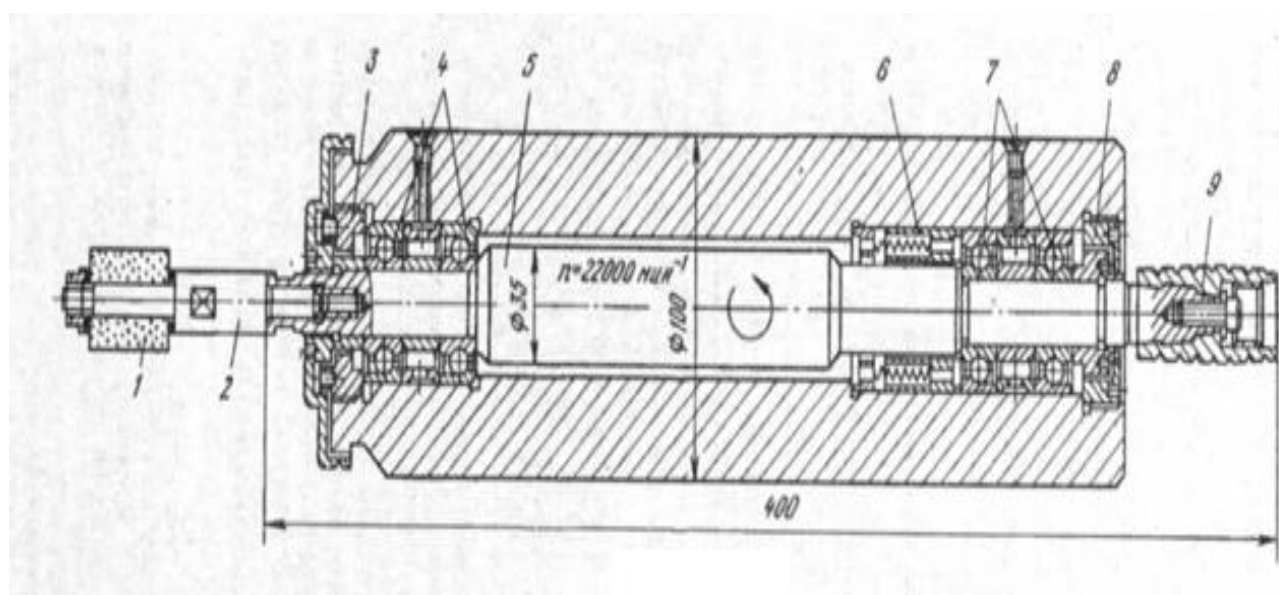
Шлифовальная головка внутришлифовального станка: 1 - шлифовальный круг, 2 - оправка шлифовального круга; 3,8- гайки, 4 - подшипники передней опоры шпинделя, 5 - шпиндель, 6 - пружины автоматической выборки зазора в задней опоре шпинделя, 7 - подшипники задней опоры шпинделя, 9 - шкив привода шпинделя.
